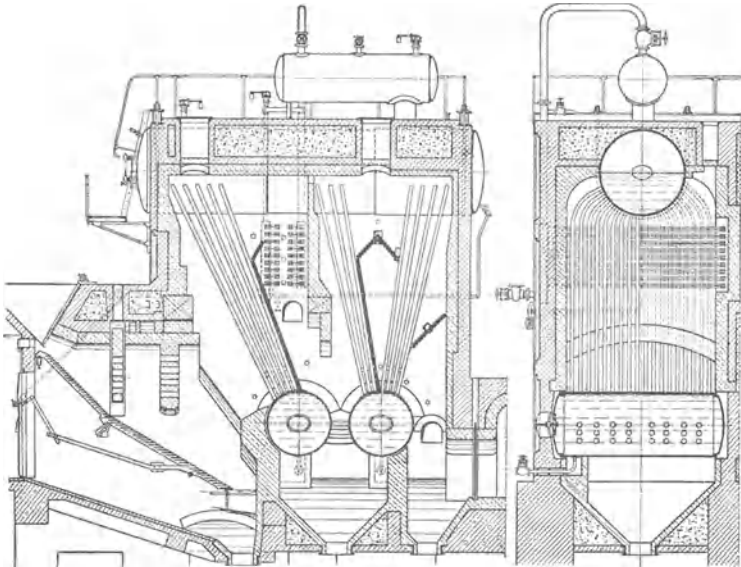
Steilrohrkessel der Maschinenbau-Anstalt Humboldt, Köln-Kalk.
